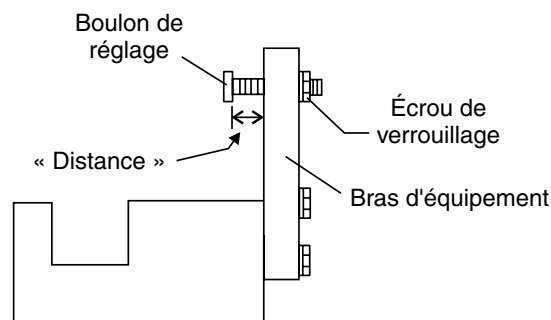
Outil de réglage du bras de la talocheuse (Vue latérale)
